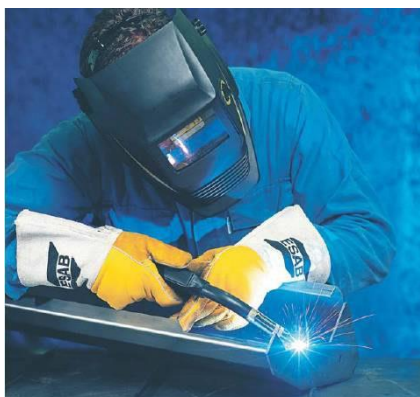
Soldagem a arco elétrico (MIG/MAG).
